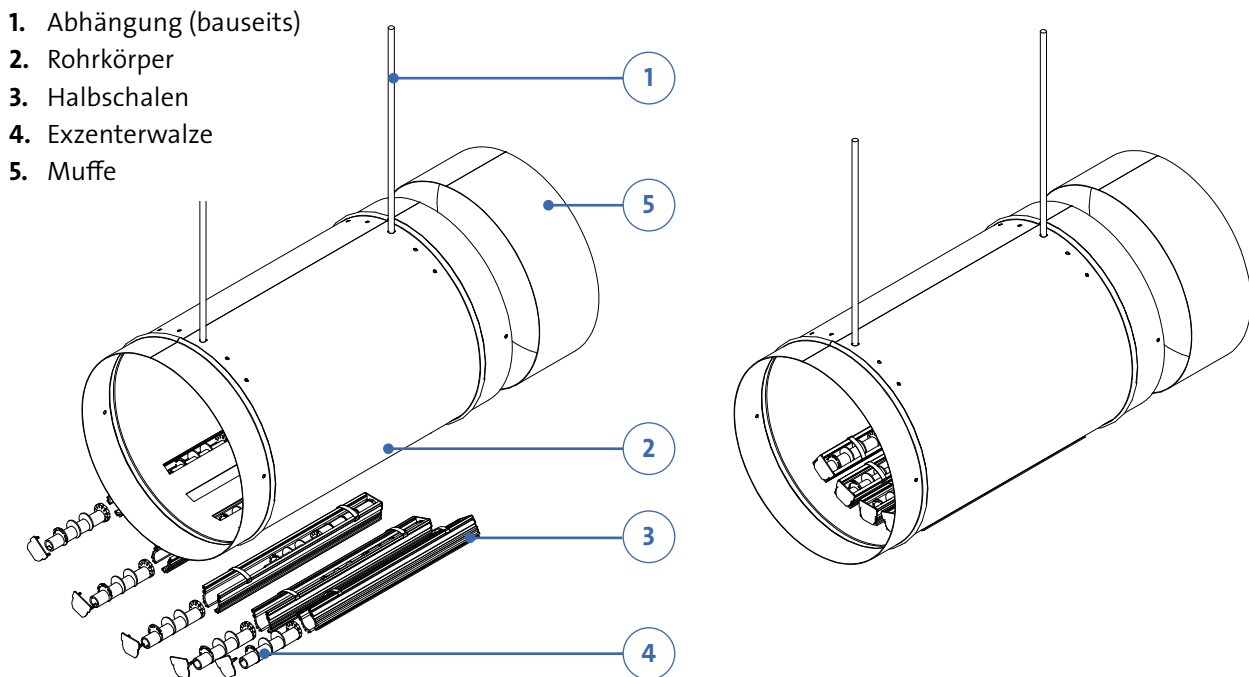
Übersicht Baugruppen Rundrohrluftdurchlass Typ RRA-5 (fünfschlitzige Variante)
